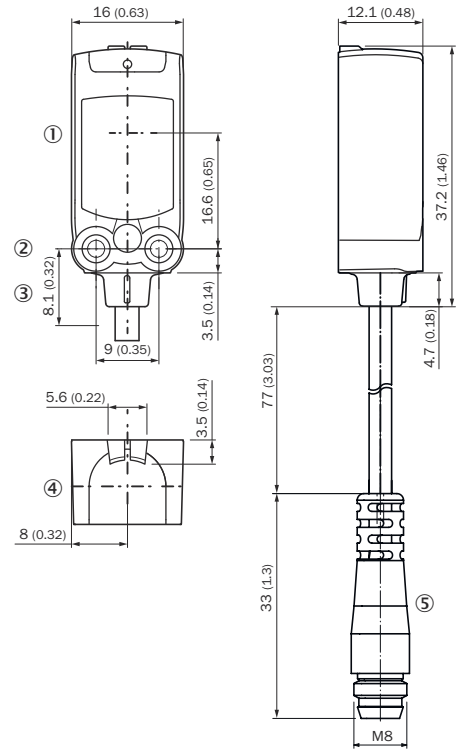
Desenho dimensional 2, cabo com conector macho M8
